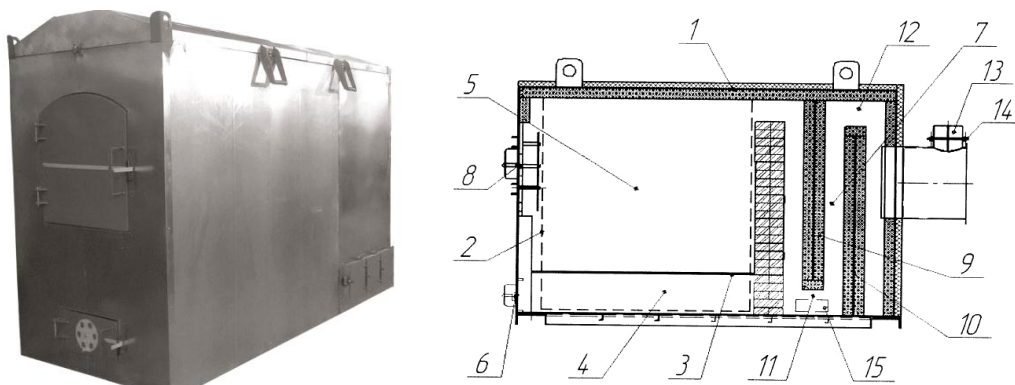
Топочный блок твердотопливный ТБТ-2500:
